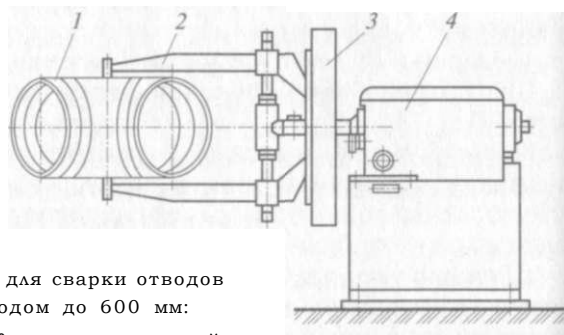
Установка для сварки отводов с условным проходом до 600 мм:
